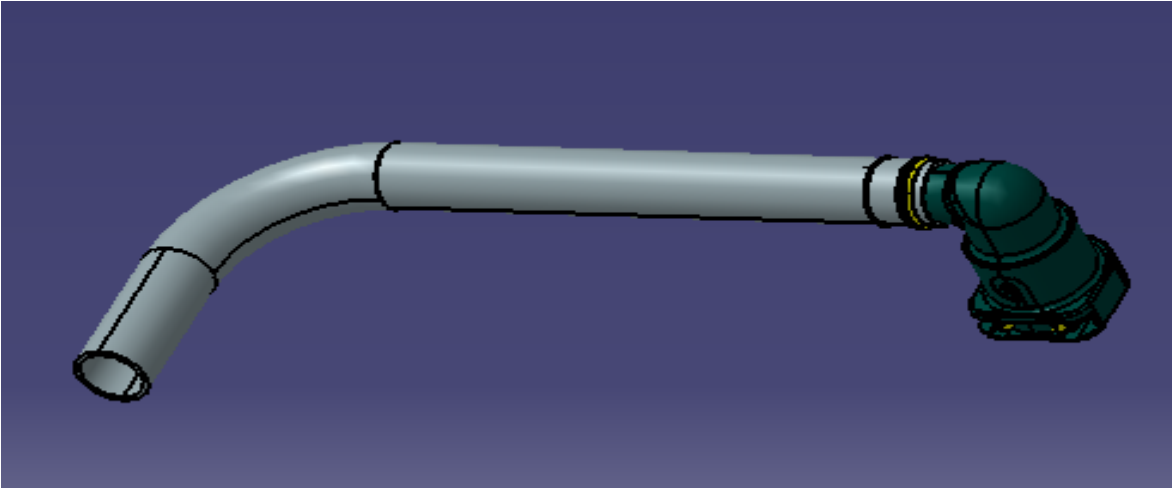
Modelo 3D de la tubería a la que se le diseñara el molde de ULTEM
